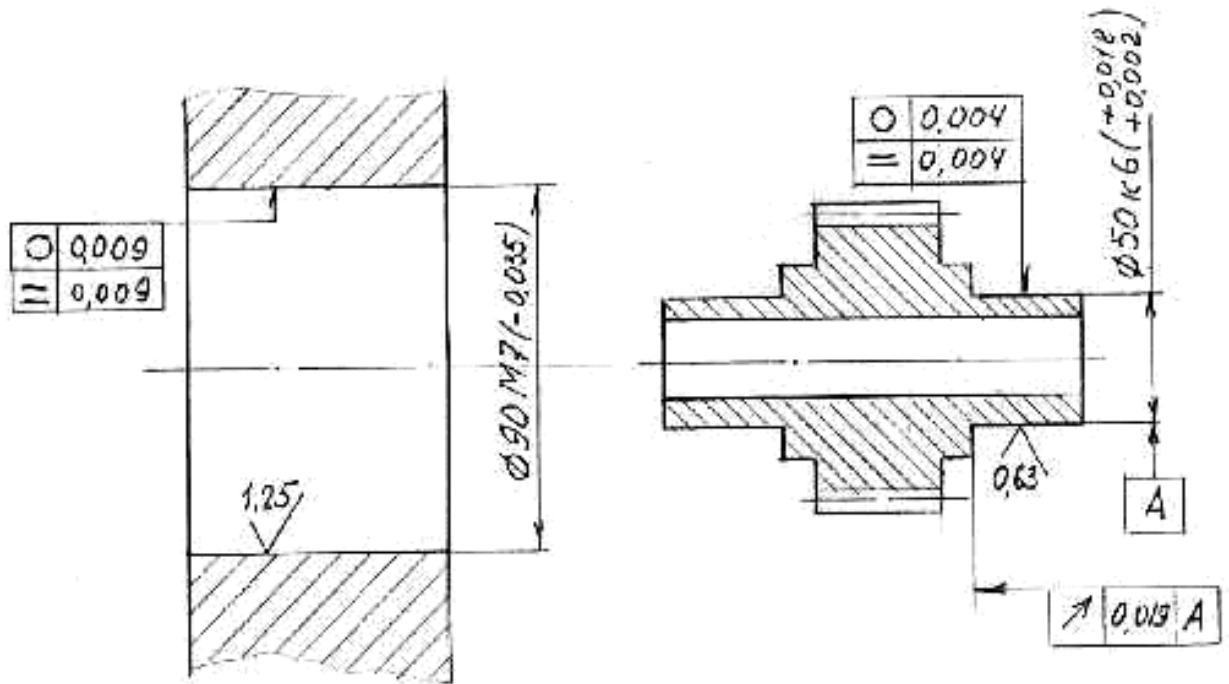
Эскизы вала и корпуса с указанием размеров и допусков формы и расположения посадочных поверхностей.
